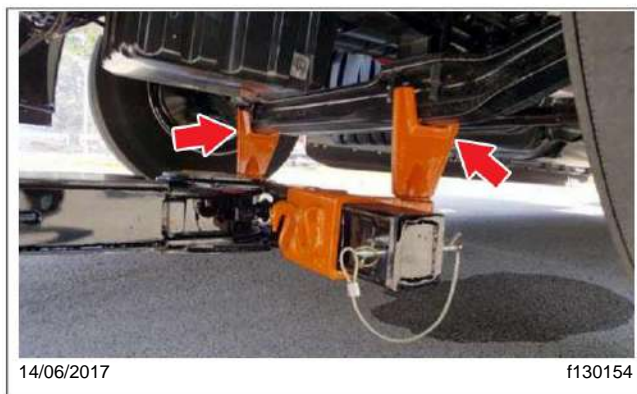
, Colocación del Stinger con adaptadores de elevación debajo del eje
